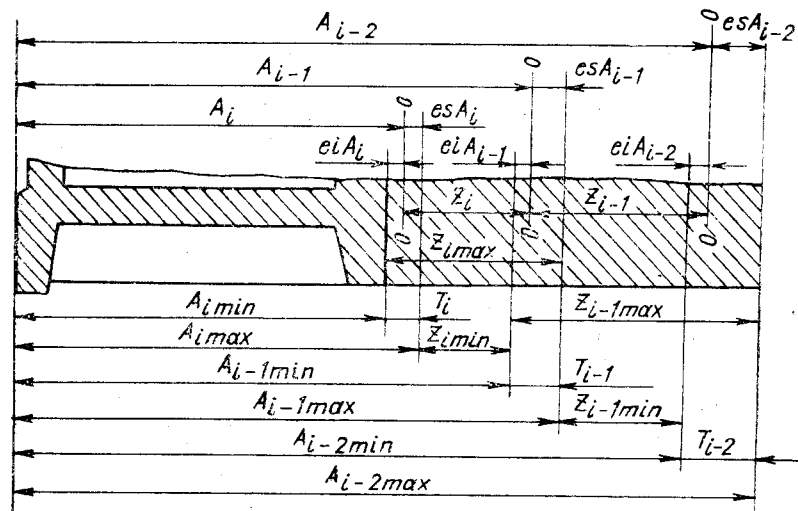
Схема розмірів, припусків та їх відхилень для заготовок.
